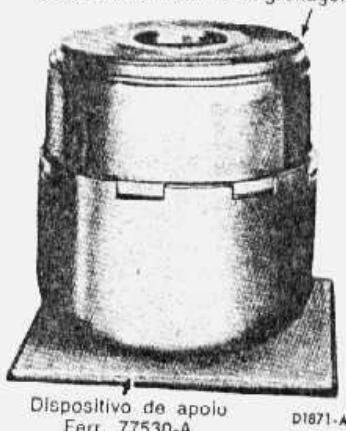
trem de engrenagens apoiado sobre o dispositivo
